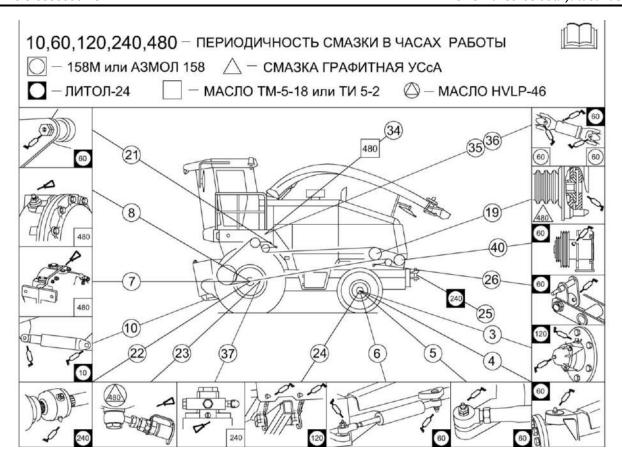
Схема смазки измельчителя (вид слева)
